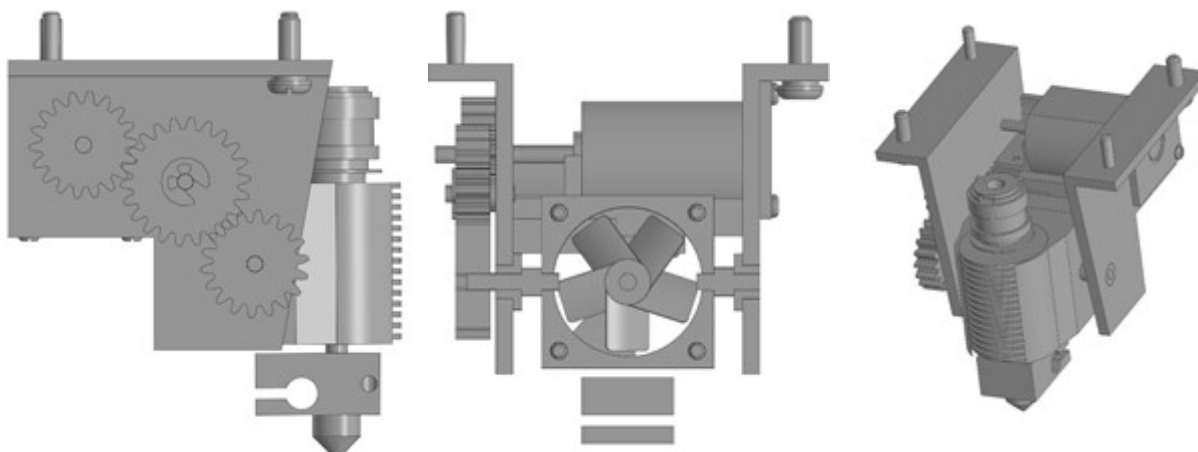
3D модель конструкции поворотного экструдера [8]
